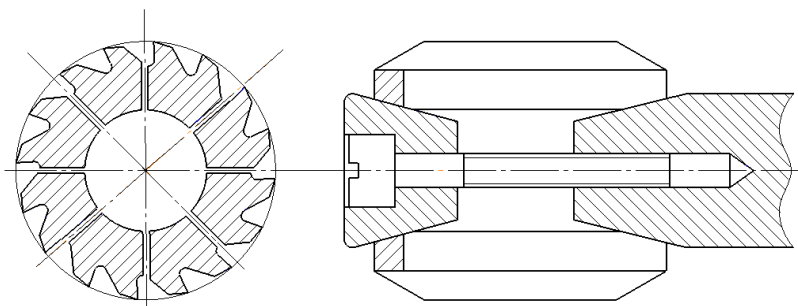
Регулируемая развертка с четырьмя прорезями
